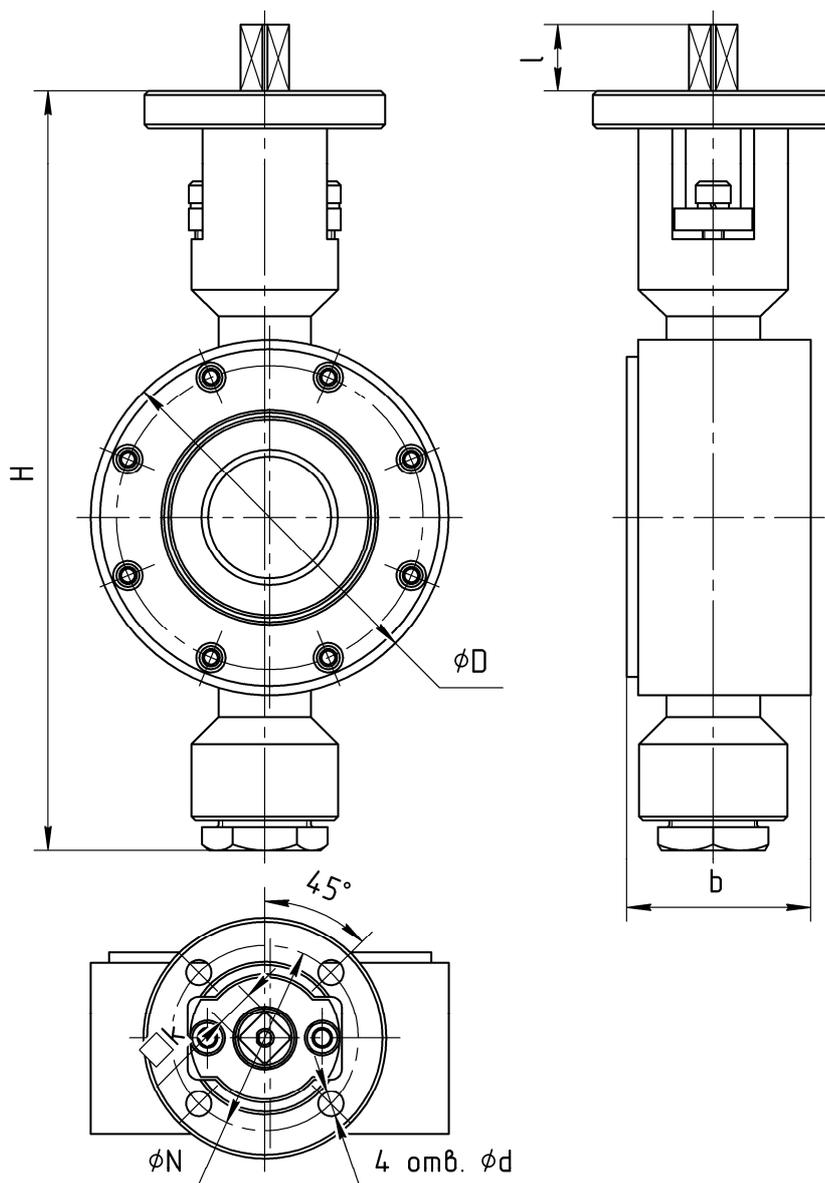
Габаритные и присоединительные размеры затвора с двойным эксцентриситетом
